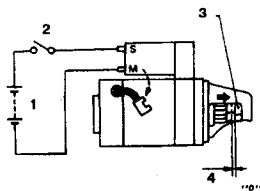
Выступ ведущей шестерни стартера S114-316 (См. Раздел 12)
